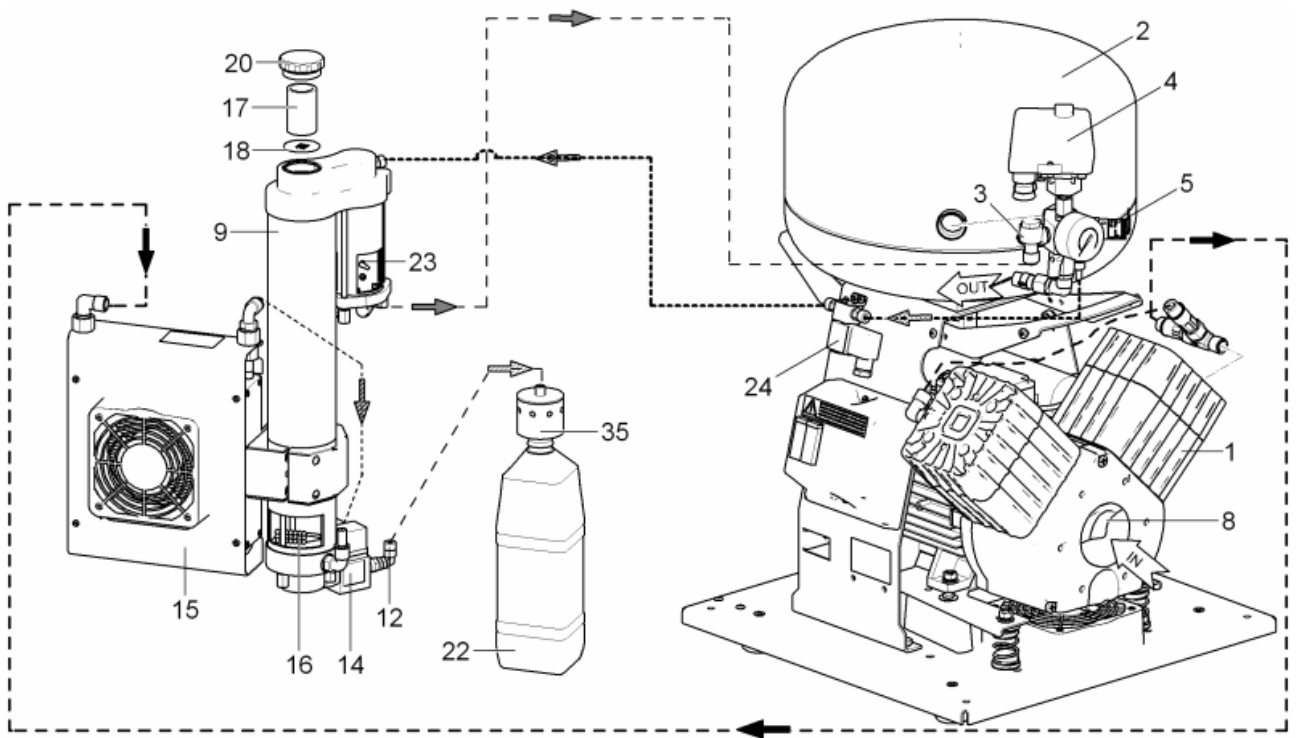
Kompressor mit Lufttrockner MONZUN – M2
